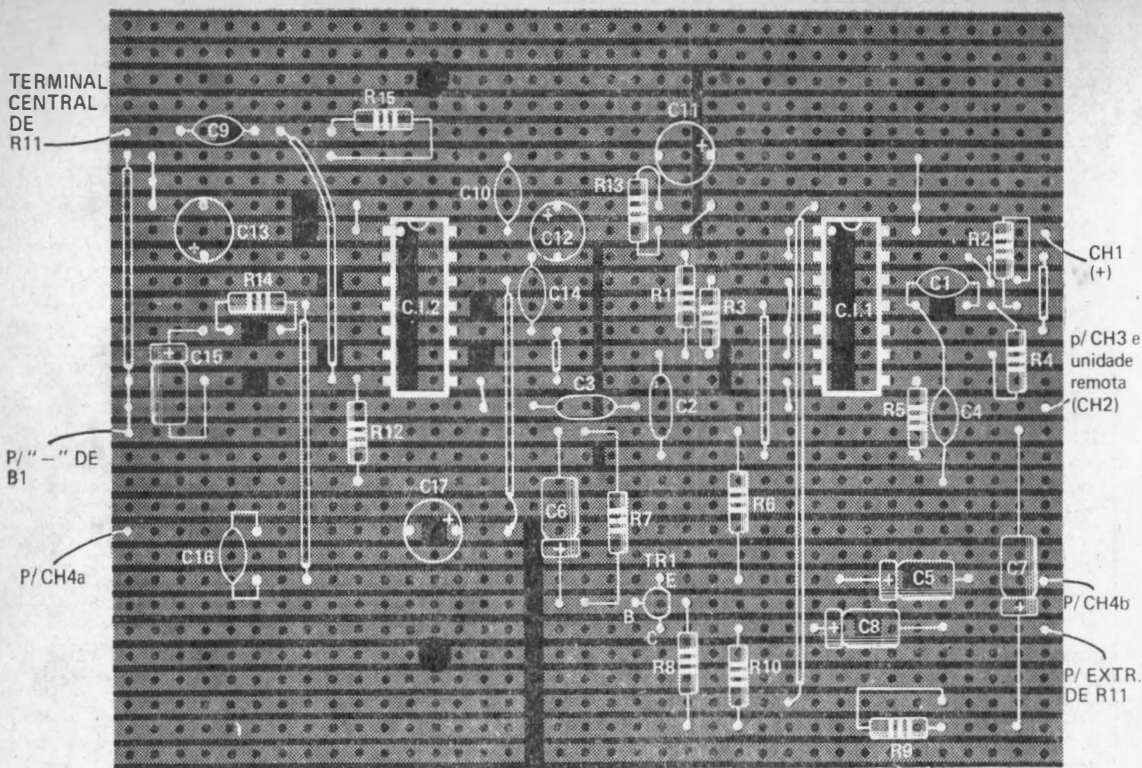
Situação dos componentes sobre a face não cobreada da plaqueta de circuito impresso da Fig. 2.
